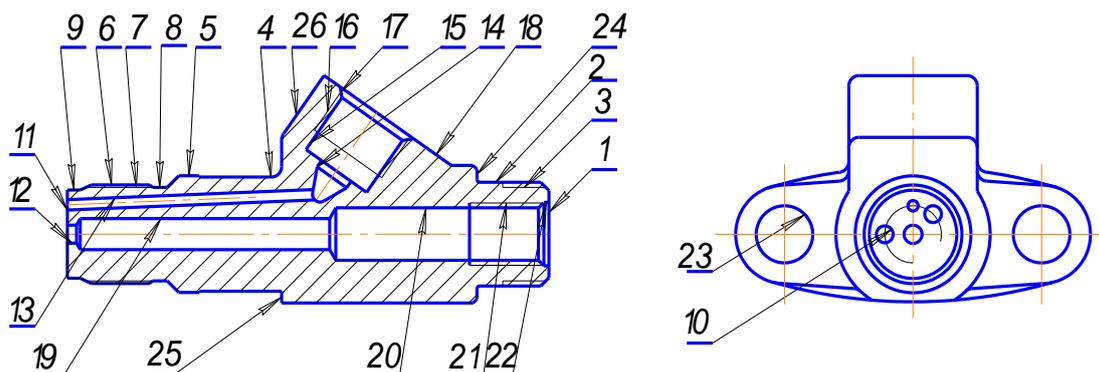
Эскиз корпуса форсунки для классификации поверхностей
